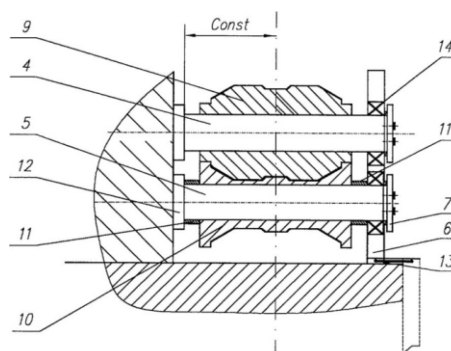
Профилегибочный станок, сечение А-А [3]:
